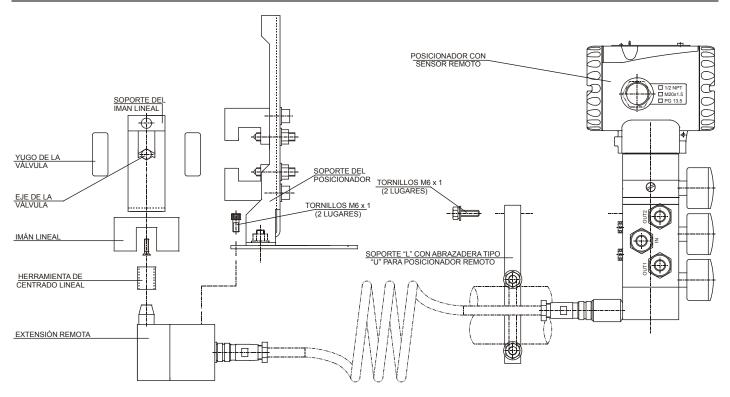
Posicionador en Actuador Lineal con Sensor de Posición Remoto
